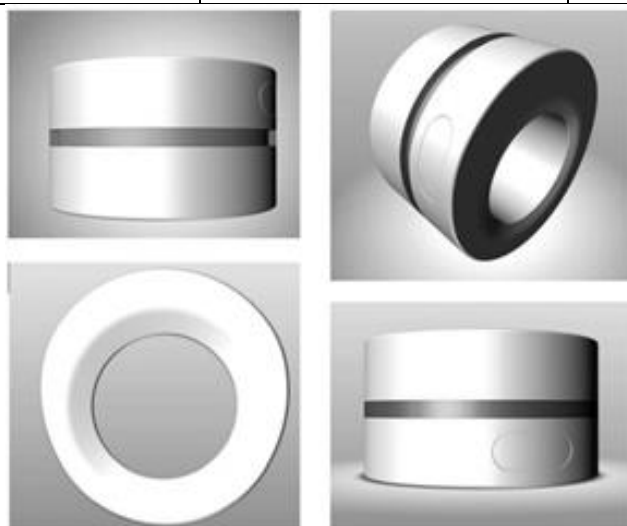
Модель корпуса устройства размеров 17 мм.
